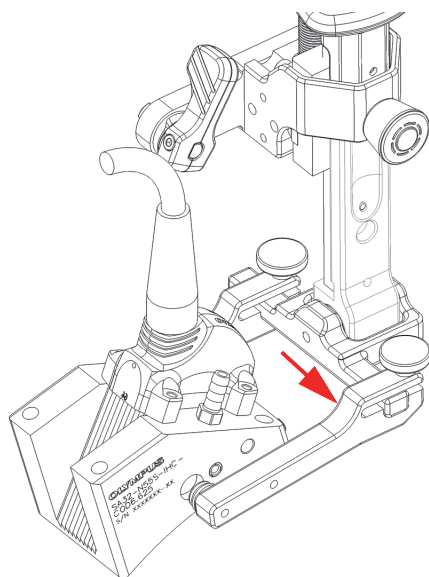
Сдвиг рычага вилки к краю стержня вилки
